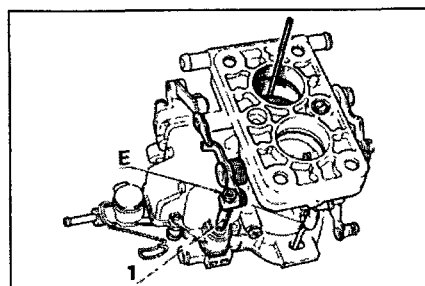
Регулировка клапана вентиляции поплавковой камеры
